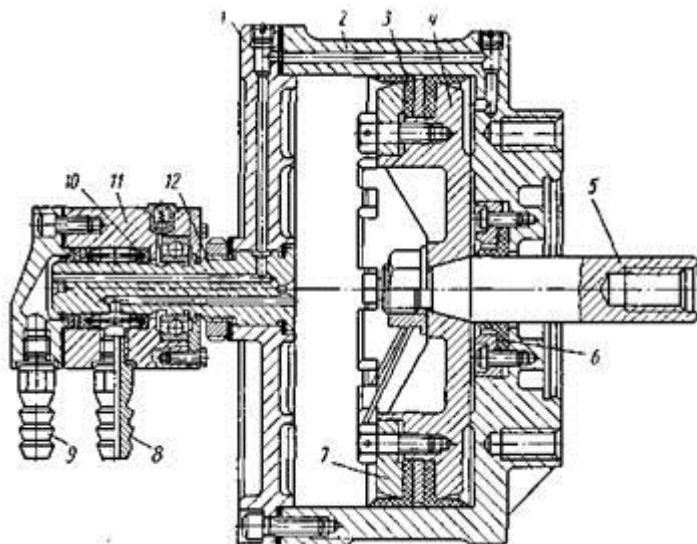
Вращающийся поршневой пневмопривод двустороннего действия
